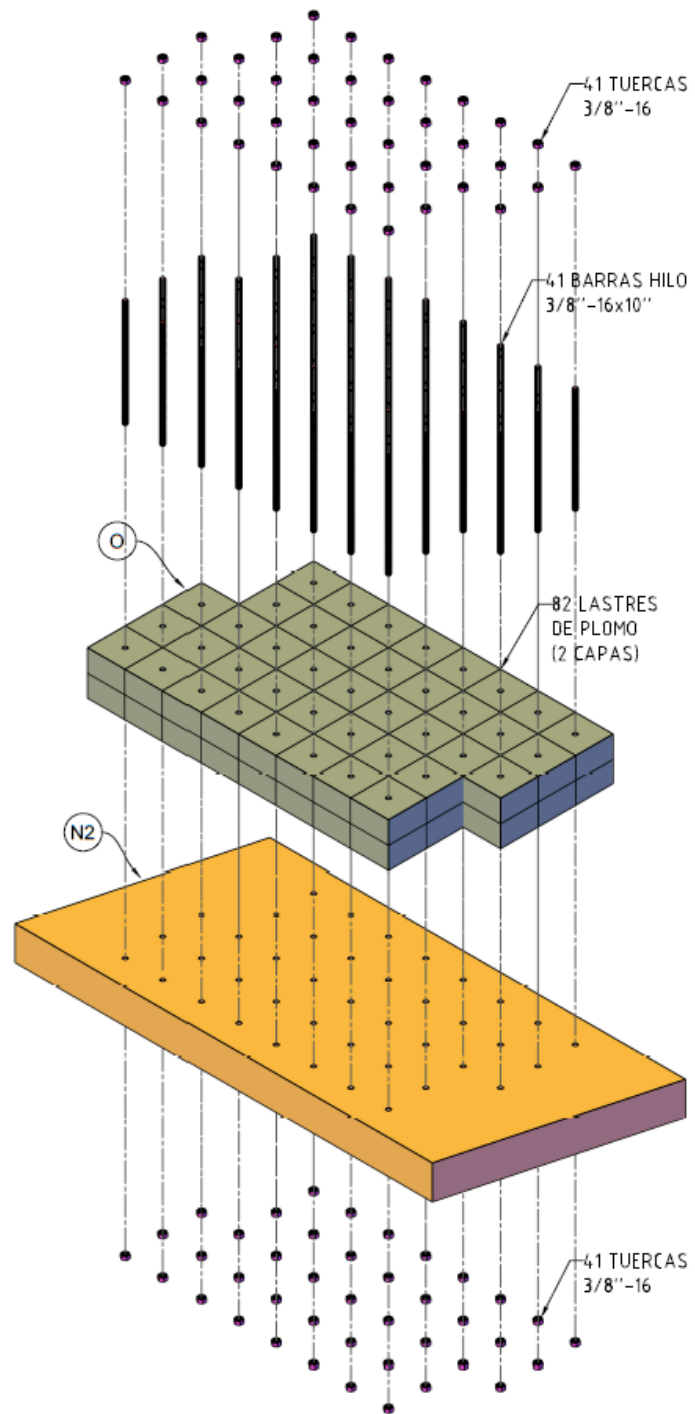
Plano de Montaje: Sistema Tablero M-0.
